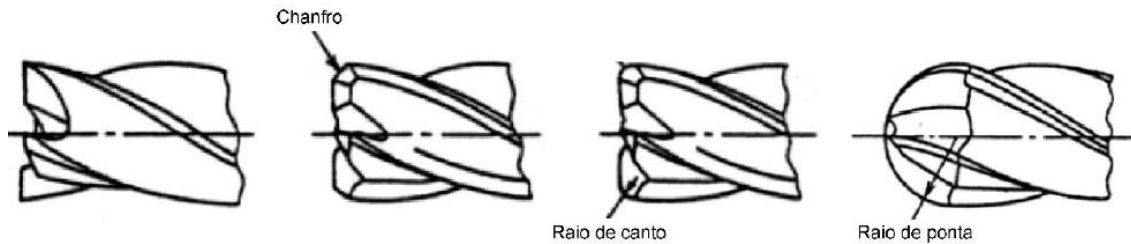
Ponta das fresas monobloco para operações de fresagem (adaptado de [27])
